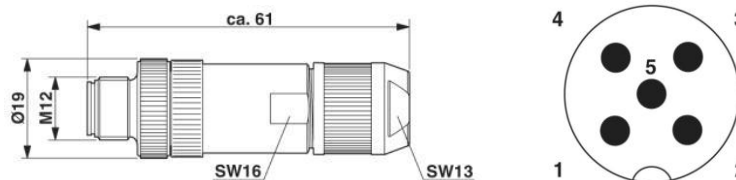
Stecker M12 x 1 gerade, geschirmt ; Polbild Stecker M12, 5-polig, A-kodiert, Ansicht Stiftseite, Phoenix Bezeichnung: SACC-M12MS-5SC
